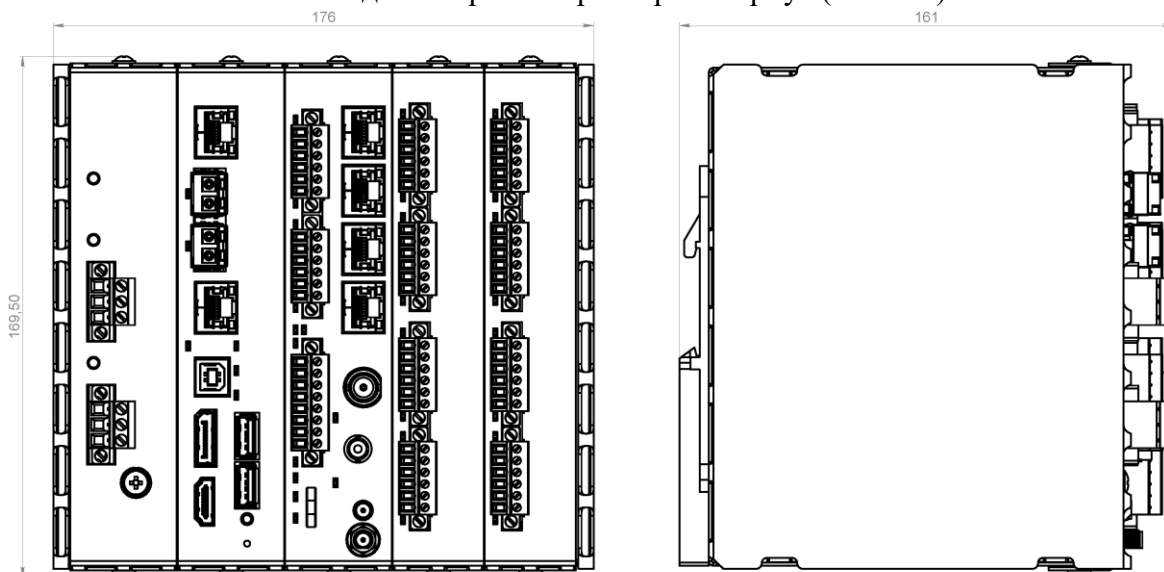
Внешний вид и габаритные размеры - корпус (ШхВхГ) 180 x 180 x 170 мм.
